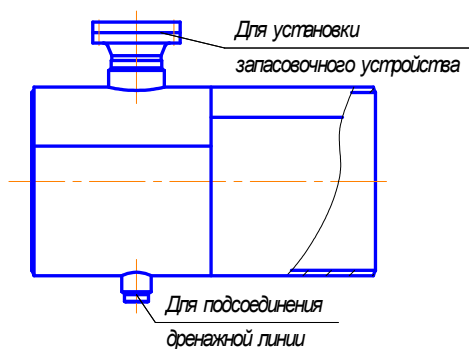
Вставка в номинальную часть камеры с патрубками для установки запасовочного устройства и присоединения дренажной линии
